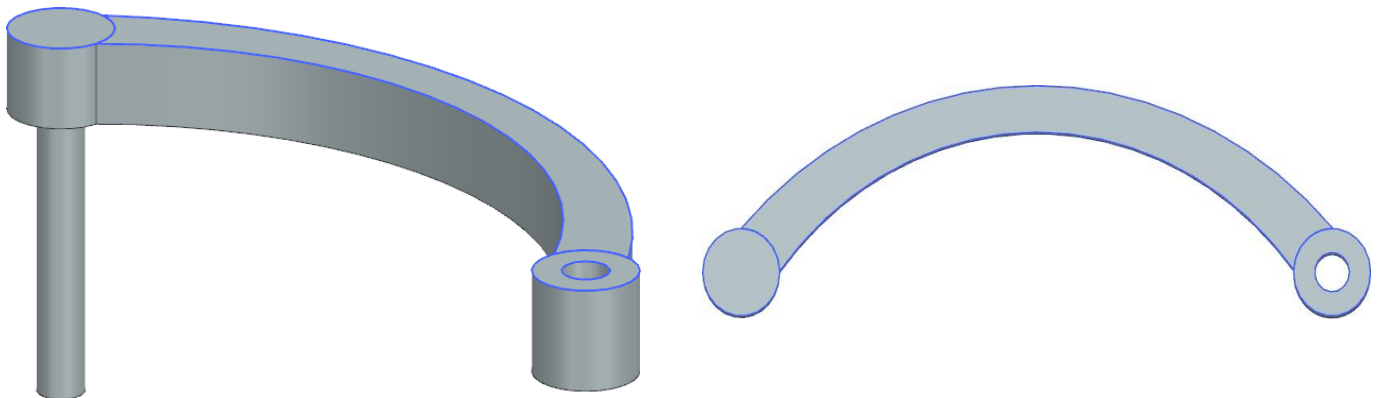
y 53. Diseño en CAD del diseño de la extensión.
